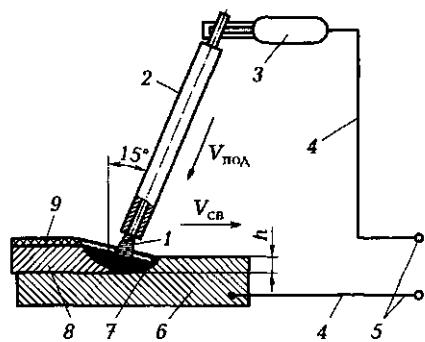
Схема ручной дуговой сварки покрытым электродом:
